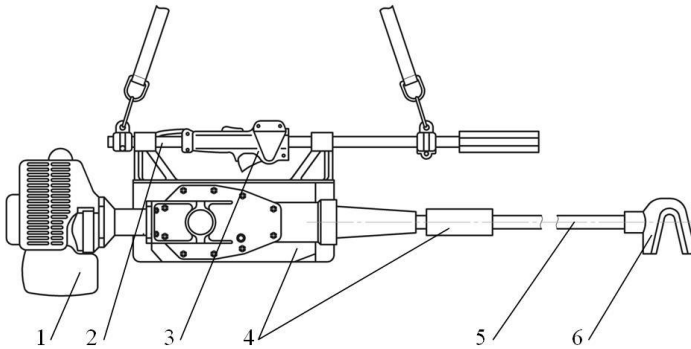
Принципова схема ручного віброударного струшувача плодів: 1 – двигун; 2 – механізм тримання і маневрування струшувачем; 3 – регульована ручка керування двигуном; 4 – збурювач віброударних коливань; 5 – штанга; 6 – захват
